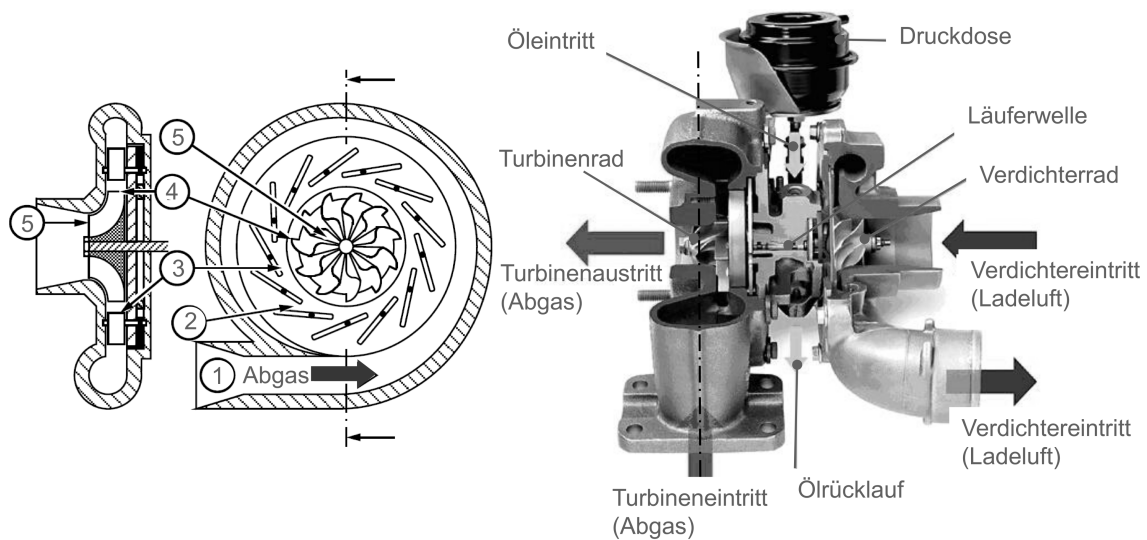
Aufbau des Abgasturboladers mit variabler Turbinengeometrie [111, 119]
